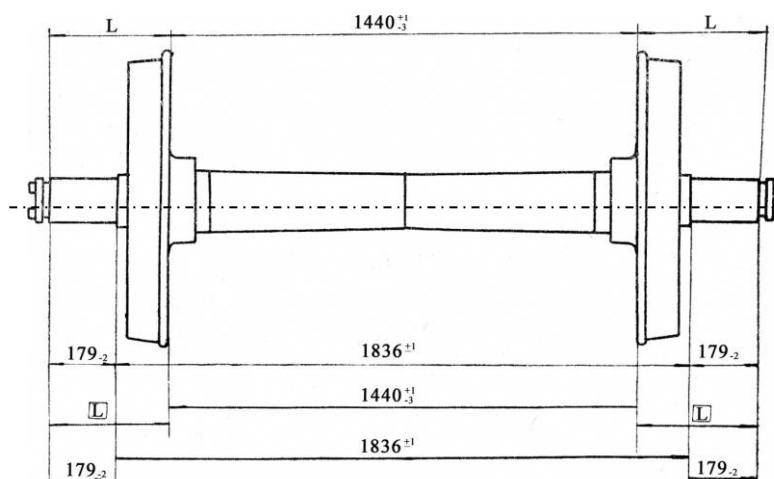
Колесная пара вагона с колесами $\varnothing 950$ мм и схема размерной цепи
